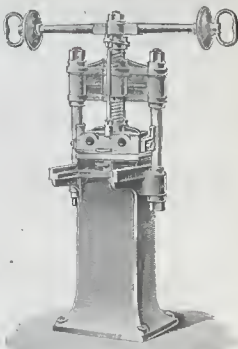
Vergoldpresse mit Schraubgewinde von Hebeln des. des. in Elmsbü. a. H.
